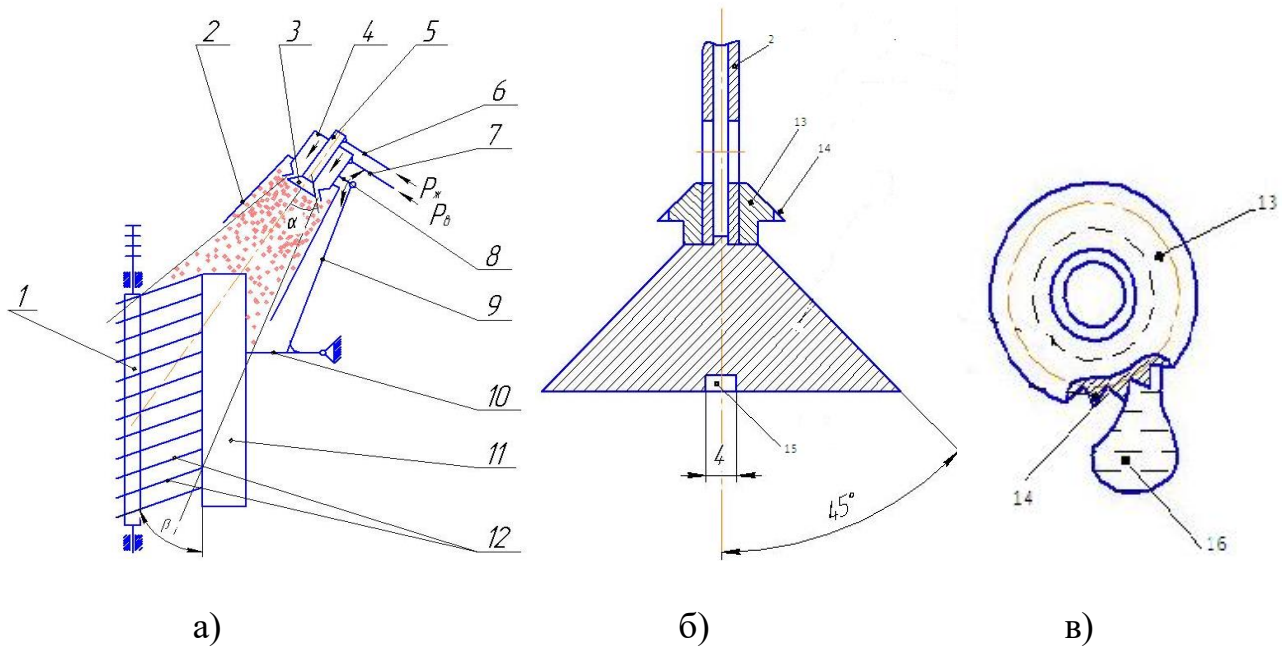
Схема приспособления для гидромеханической очистки шпинделей: 1- вертикальный шпindel; 2-направитель каплесодержащего потока; 3-расширитель потока, 4-аэровихревой кавиатор – увлажнитель; 5-центральная перфорированная трубка; 6,7-жидкостновоздушная коммуникация, 8,9,10-кронштейны; 11-планка; 12-щеточные элементы; 13- турбулизатор; 14-зубец; 15-регулируемый паз; 16-одиночная капля; α -угол раскрытия расширителя потока; β -угол наклона ворса щеточного элемента; а-схема установки устройства для гидромеханической очистки относительно шпинделя, б-схема установки турбулизатора на центральную трубку, в-горизонтальная проекция турбулизатора.
